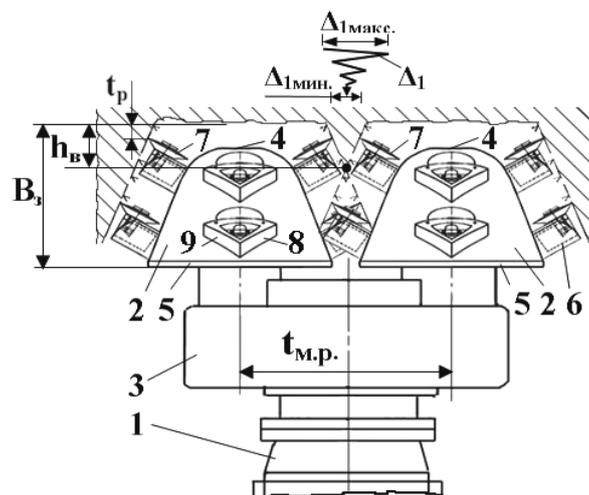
Двухкорончатый исполнительный орган реверсивного действия
